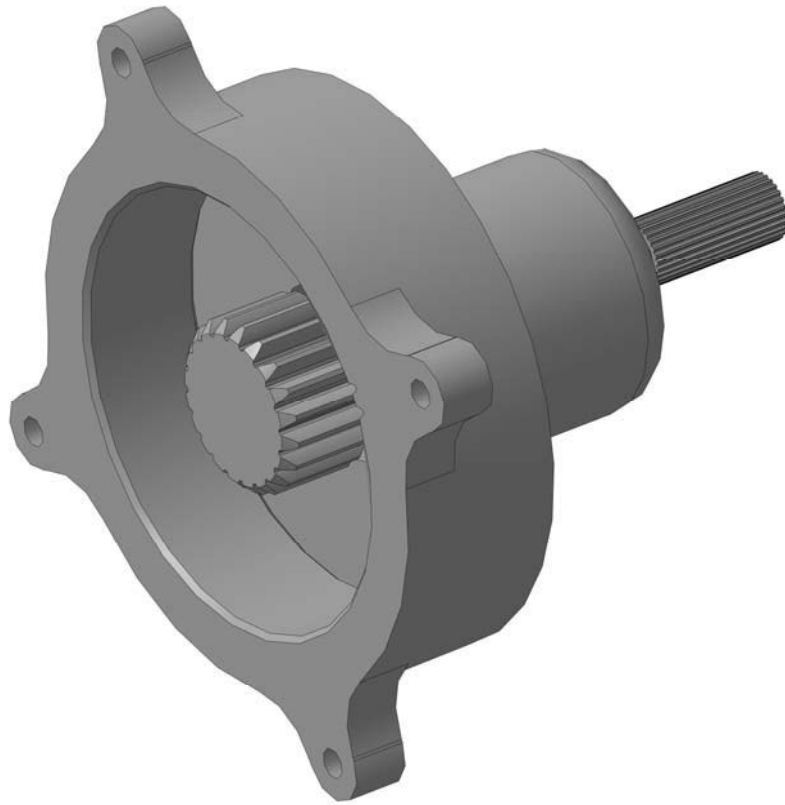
Сборка корпуса редуктора и вал-шестерни
